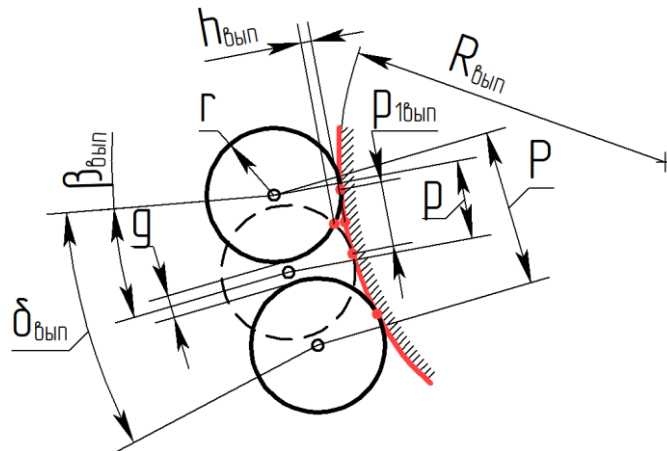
Схема расположения СМП на выпуклой поверхности обрабатываемой детали.
